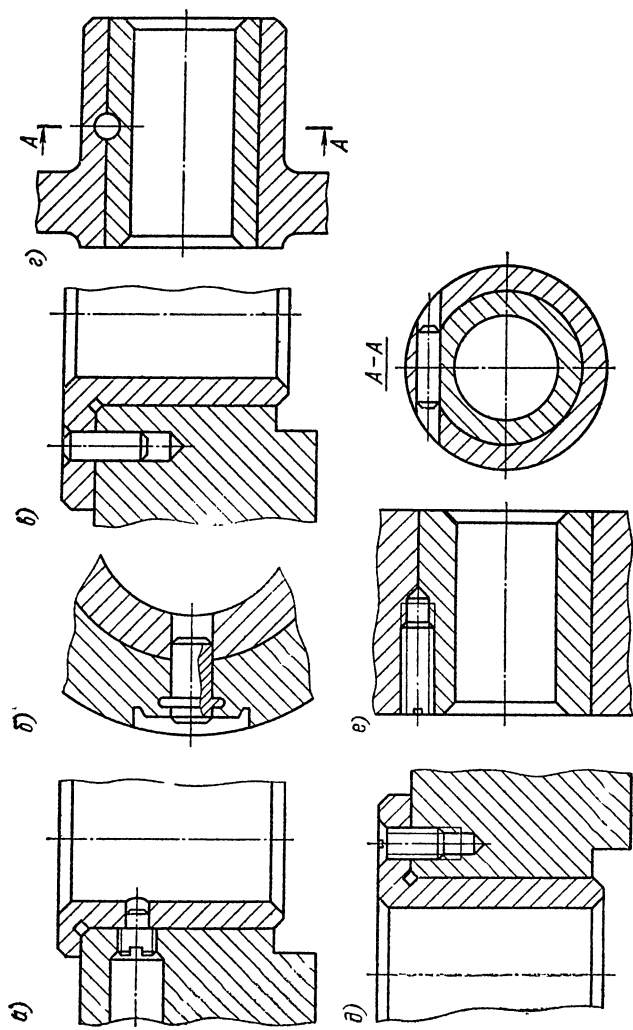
Некоторые способы крепления втулок от проворачивания: а, б, в — винтами; б...з — штифтами
